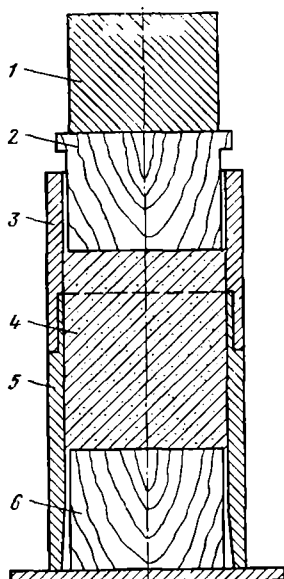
Схема приспособления для изготовления образцов при измерении газопроницаемости
